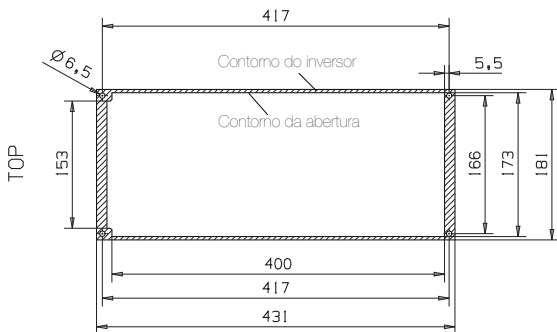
Dimensões do recorte para montagem com flange do MR4 ao MR6 (unidade: mm)
